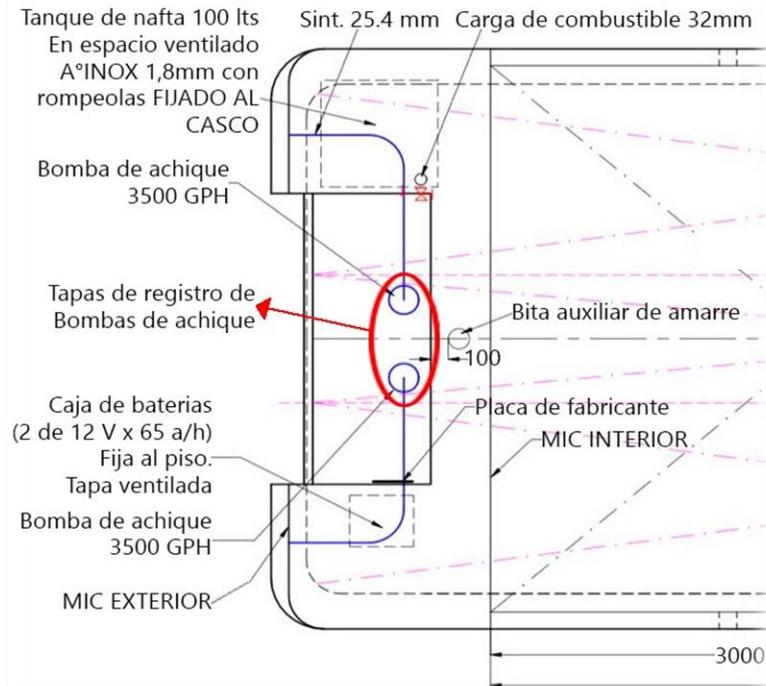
Vista de planta de la cubierta principal, sector de popa. Se destacan las tapas que no habrían estado estancas y por donde habría ingresado el agua de mar. Fuente: astillero Baader
